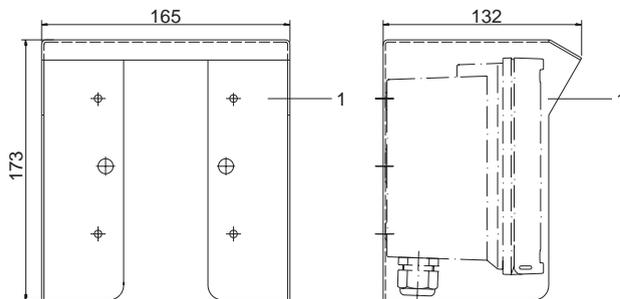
Auvent de protection ZU 0276 pour montage mural et sur mât
